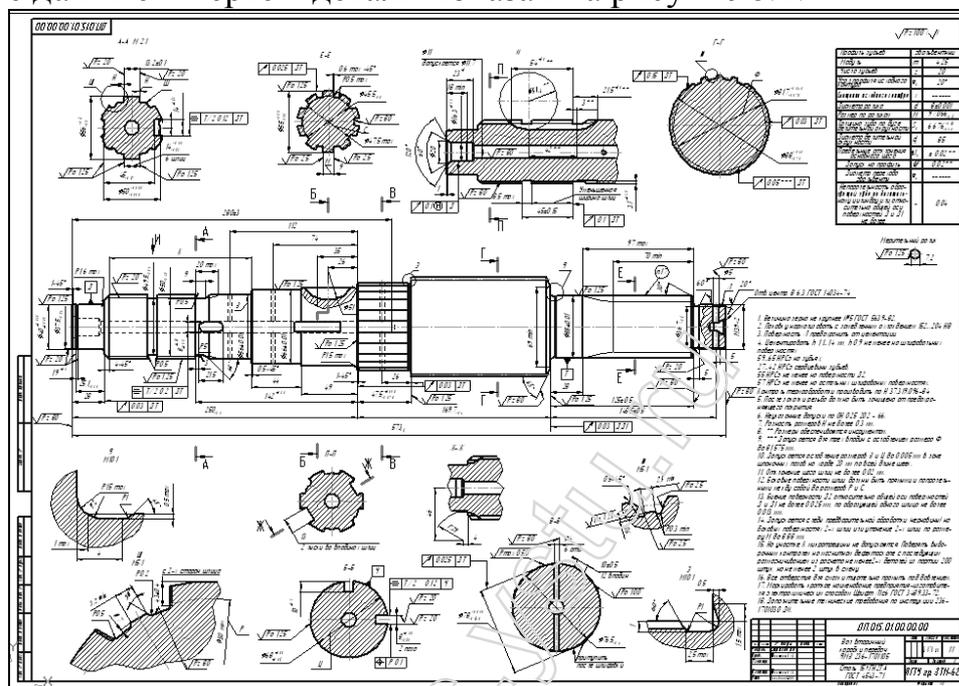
Чертеж детали «Вал05.cdw»
